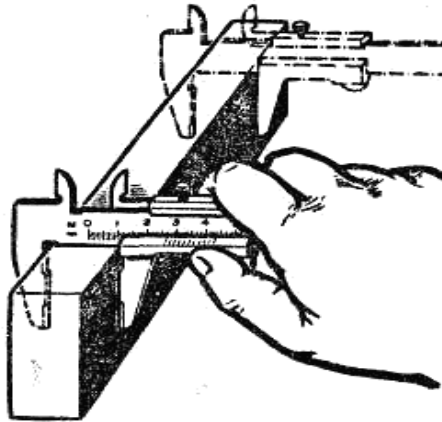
Перевірка паралельності обпилених поверхонь штангенциркулем
